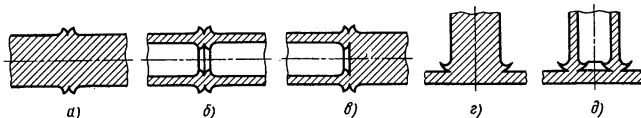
Типы соединений, выполняемых с помощью сварки трением:
